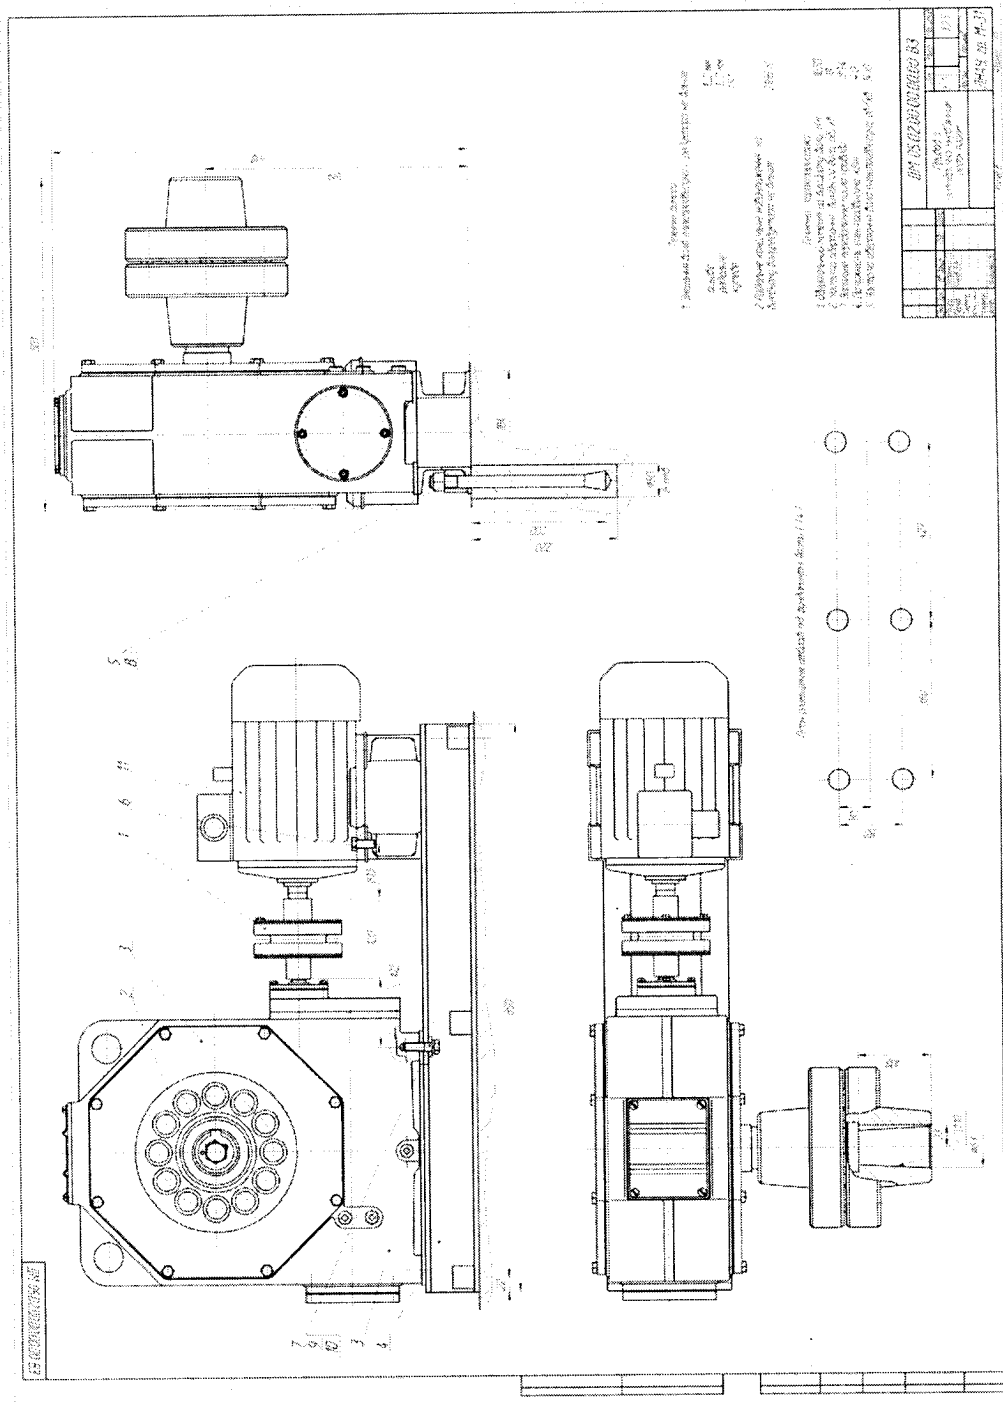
Привод з циліндрично-черв'ячним редуктором (загальний вигляд)
